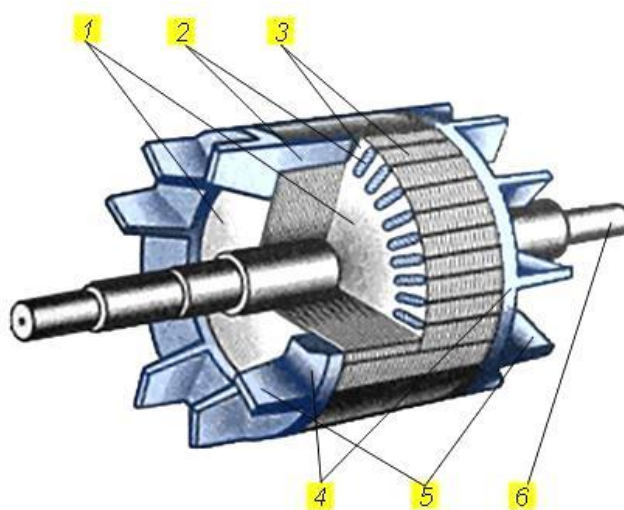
Ротор асинхронного двигателя с литой кз-обмоткой: 1 – сердечник ротора с пазами; 2 – стержни кз-обмотки ротора; 3 – зубцы сердечника ротора; 4 – КЗ-кольца обмотки ротора; 5 – вентиляционные лопатки; 6 – вал
